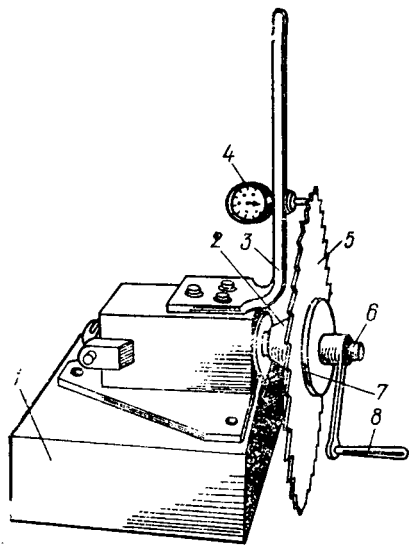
Приспособление ПН для проверки качества правки круглой пилы
